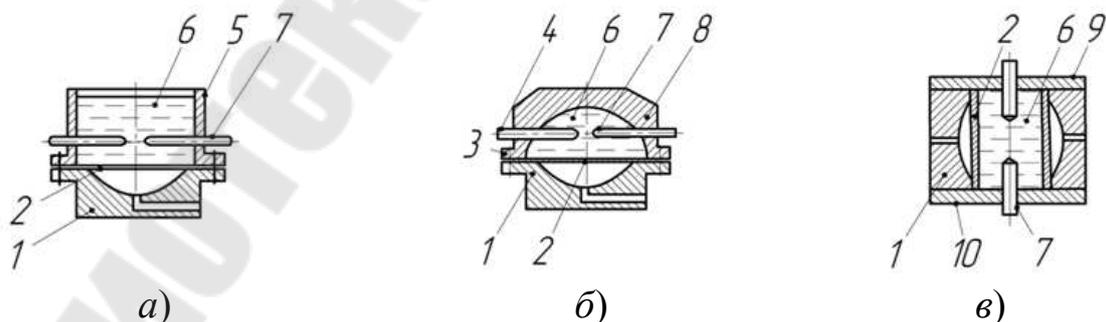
Схемы электрогидравлической штамповки деталей из плоской заготовки: а – в открытой; б – закрытой камерах; в – из трубчатой заготовки в закрытой камере; 1 – матрицы; 2 – заготовки; 3 – прижимы; 4, 7 – электроды; 5, 8 – открытая и закрытая камеры; 6 – вода; 9, 10 – верхняя и нижняя крышки
